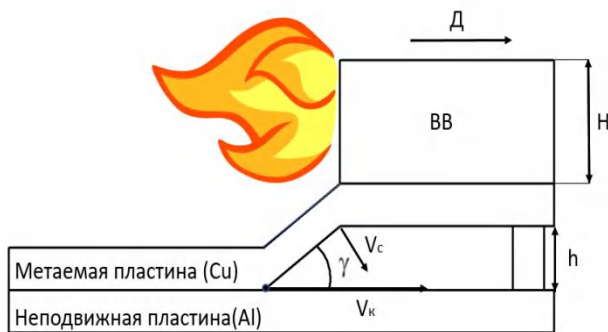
Схема соударения пластин при сварке взрывом:
